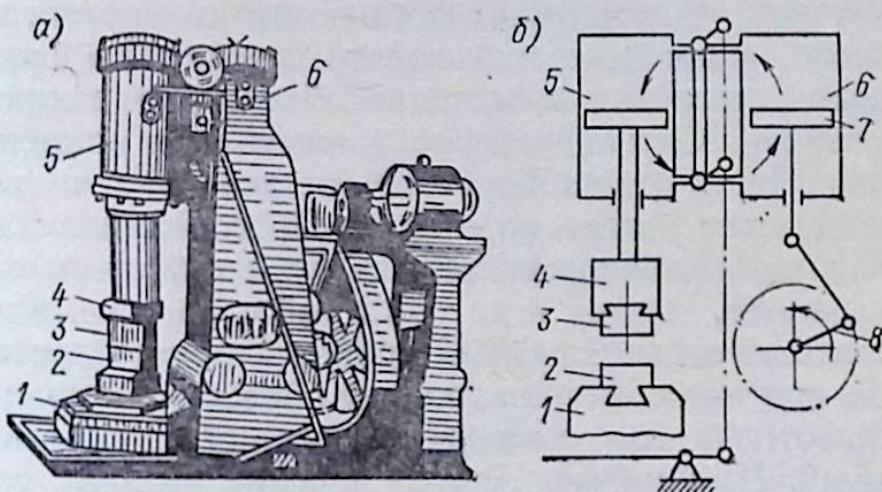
Пневматический ковочный молот: а — общий вид; б — кинематическая схема
